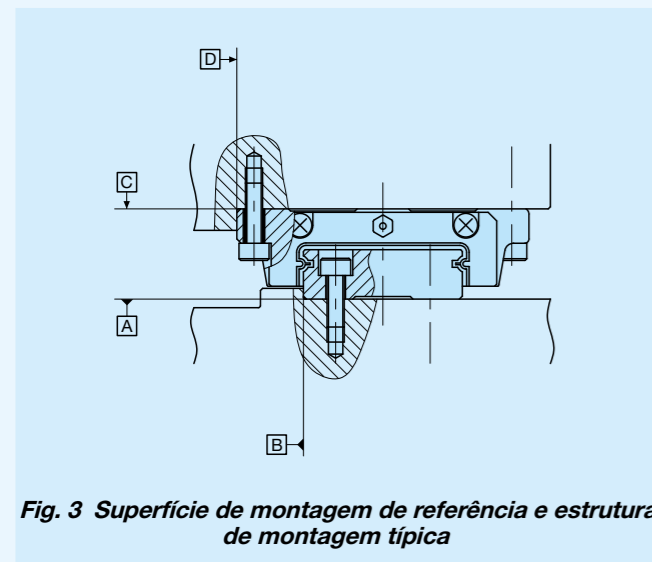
Superfície de montagem de referência e estrutura de montagem típica
